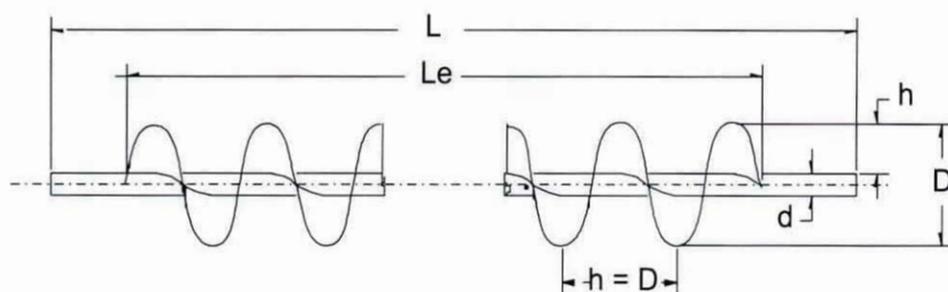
Dimensiones principales del rotor del transportador de un tornillo sinfín.
